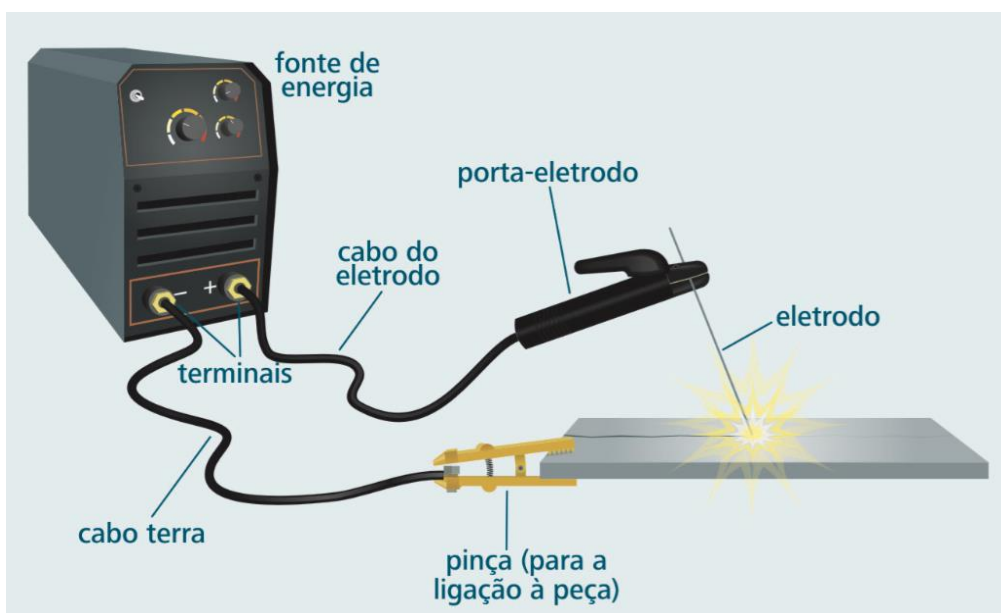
Esquema da soldagem por eletrodo revestido [45].
